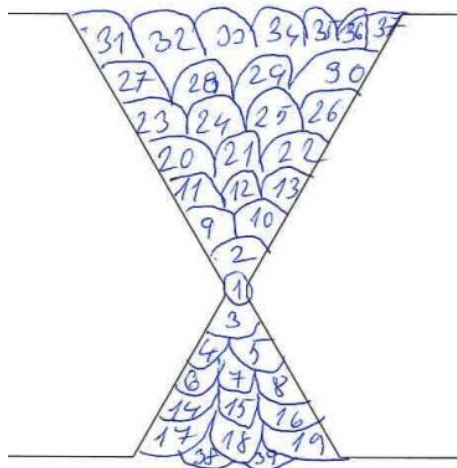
Způsob kladení housenek – vzorek 1
